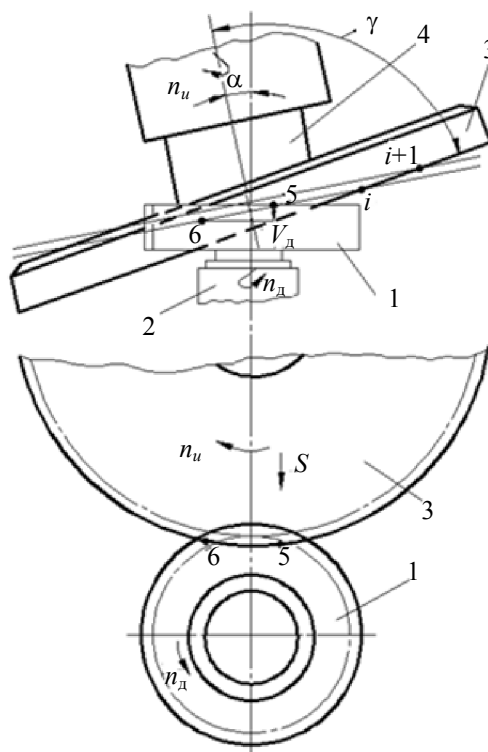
Схема формирования цилиндрических наружных зубчатых поверхностей специальным долбяком: 1 – заготовка; 2 – оправка; 3 – долбяк; 4 – шпиндель; 5 – позиция i -го зуба при входе на нарезание; 6 – позиция i -го зуба при выходе с нарезания
